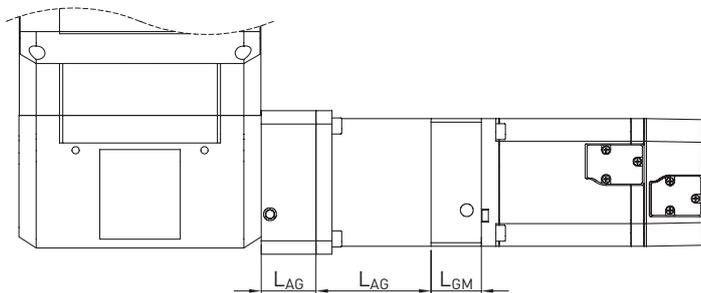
Motoranbindung Auslegerachse HC ohne Getriebe
